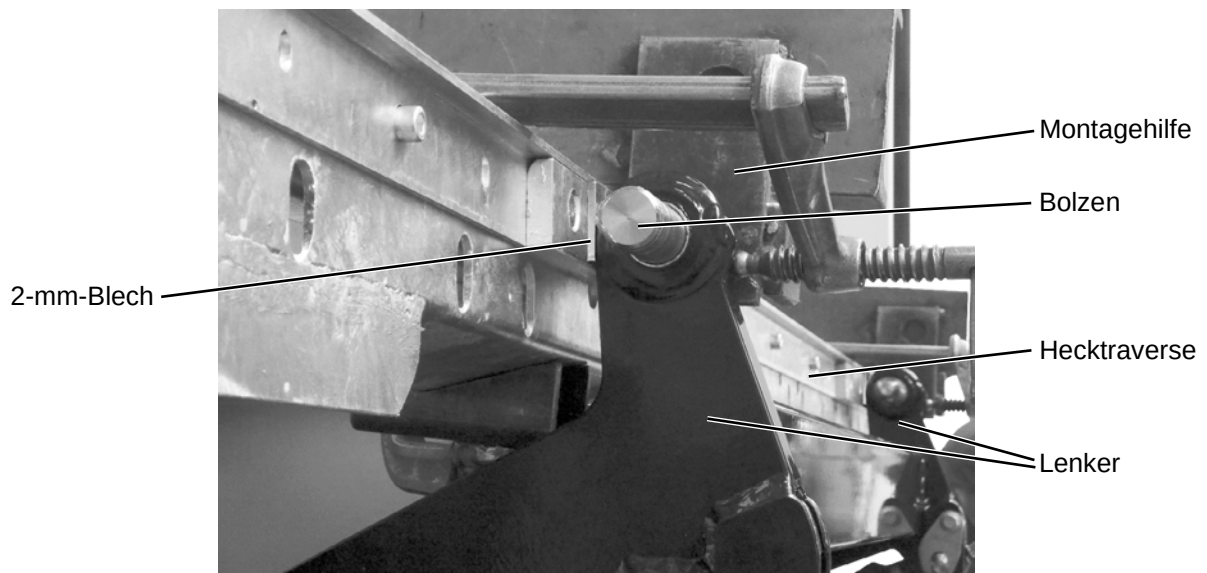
2-mm-Distanzbleche bei Montage einer beschichteten Plattform
